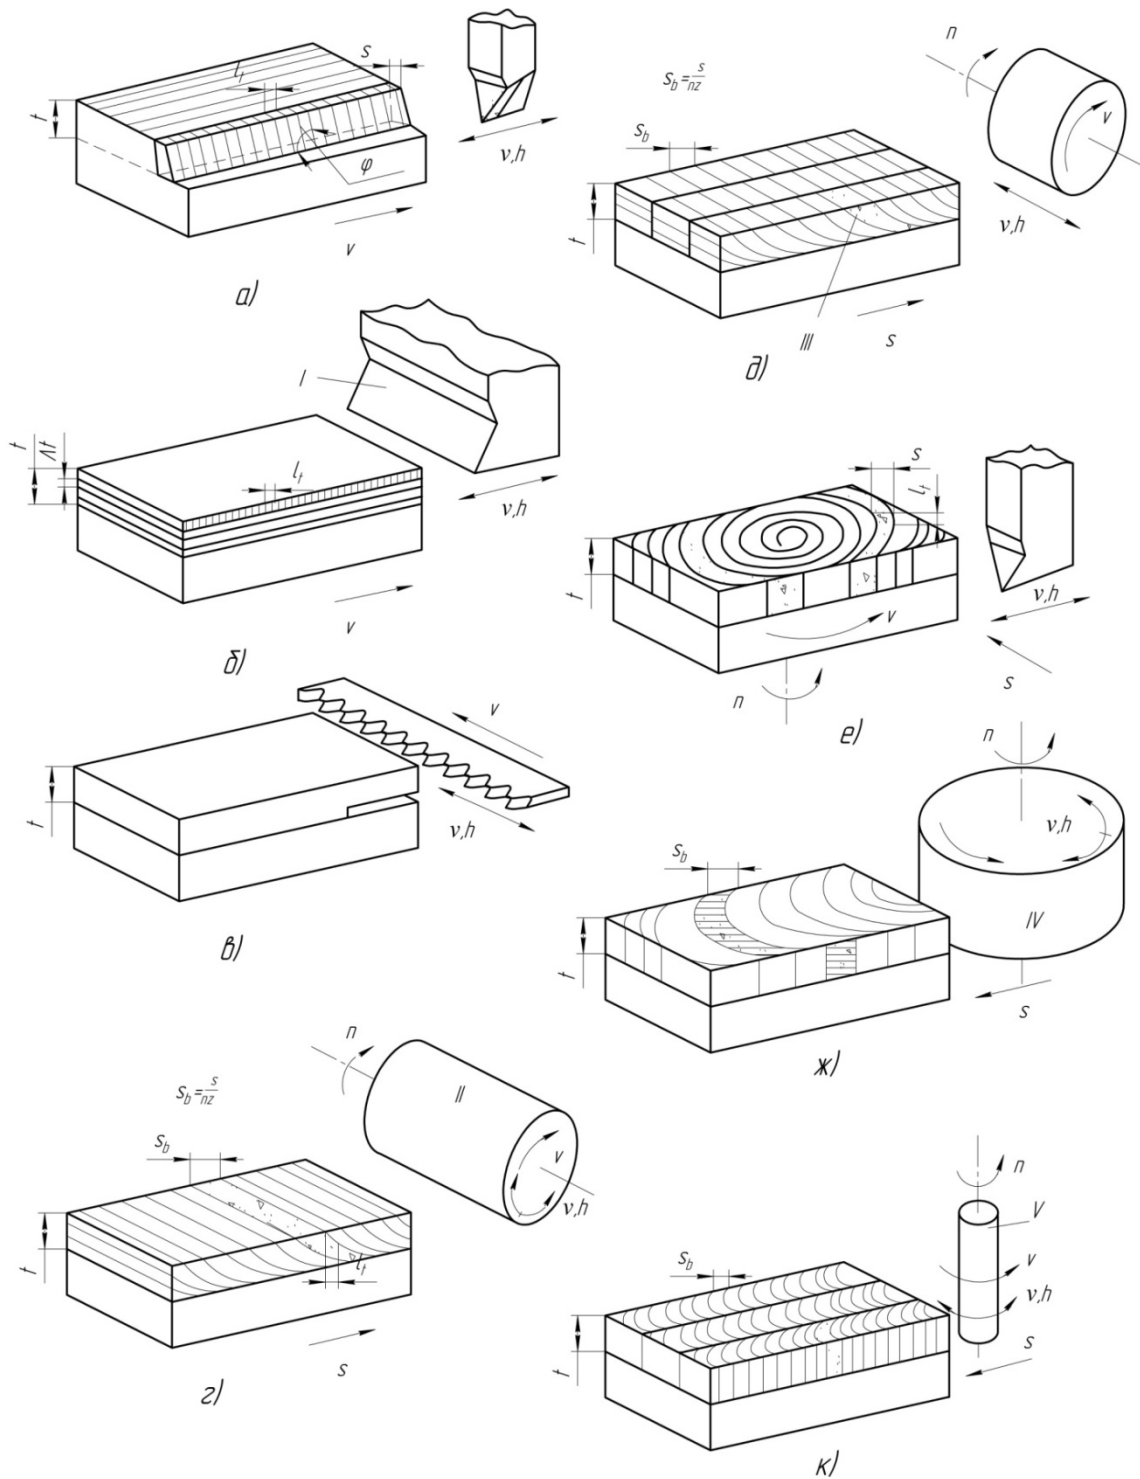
Схеми способів обробки плоских поверхонь вібраційним різанням (ν , h – частота та амплітуда вібрацій; v – напрям швидкості різання; s – напрям подачі; I – різець або зуб протяжки; II – фреза з числом зубців z ; III – механізм самоутворення поверхневих мікроканалок; IV – торцева фреза або шліфувальний круг; V – кінцева фреза)
